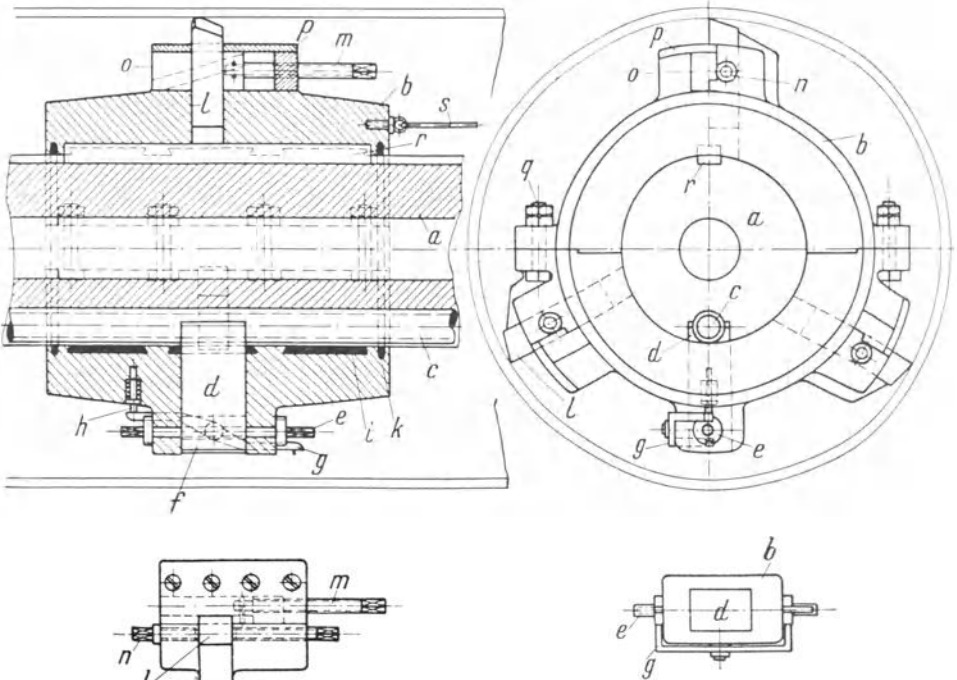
Schwerer Bohrkopf für Stahlzylinder von 500 mm Innendurchmesser.
